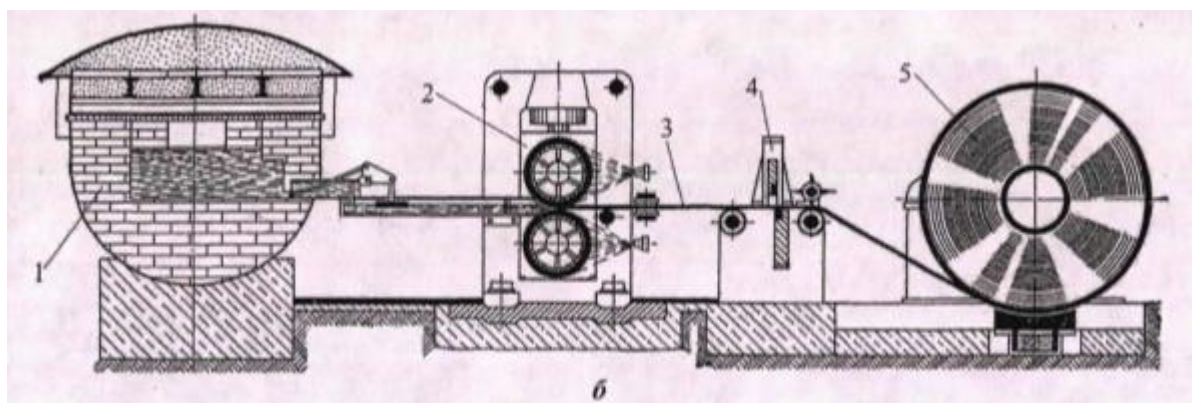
Схема установки для литья алюминиевых сплавов в двухвалковых агрегатах при подаче металла сбоку
